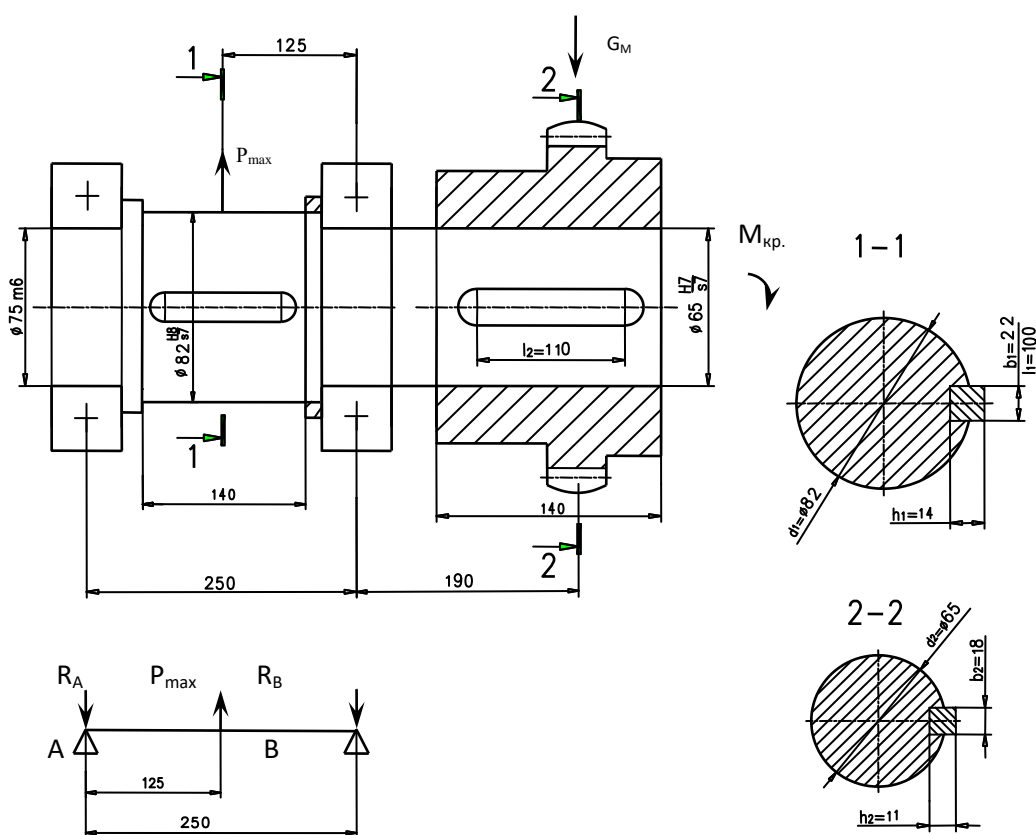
Розрахункова схема вала привідного колеса
